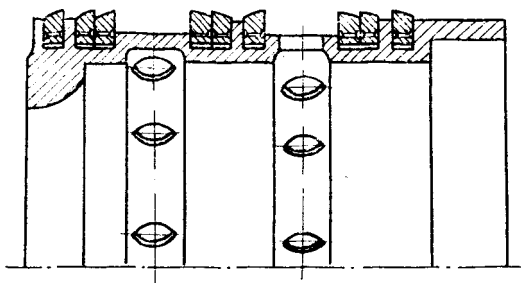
Распорная втулка упорно-опорного подшипника вала винта
